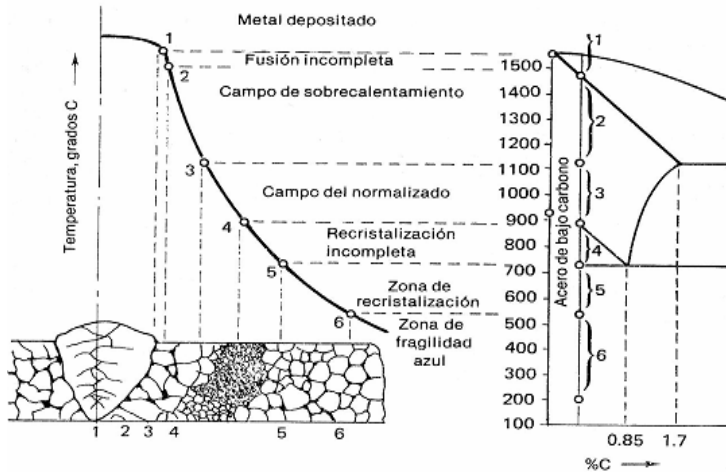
Zonas que se presentan en la ZIT de la soldadura. Fuente: Zuñiga (1983).
